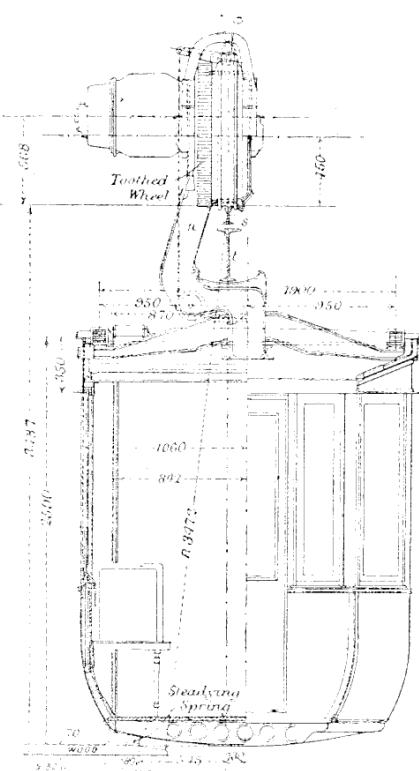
Coupe des voitures du monorail suspendu système Langen.
